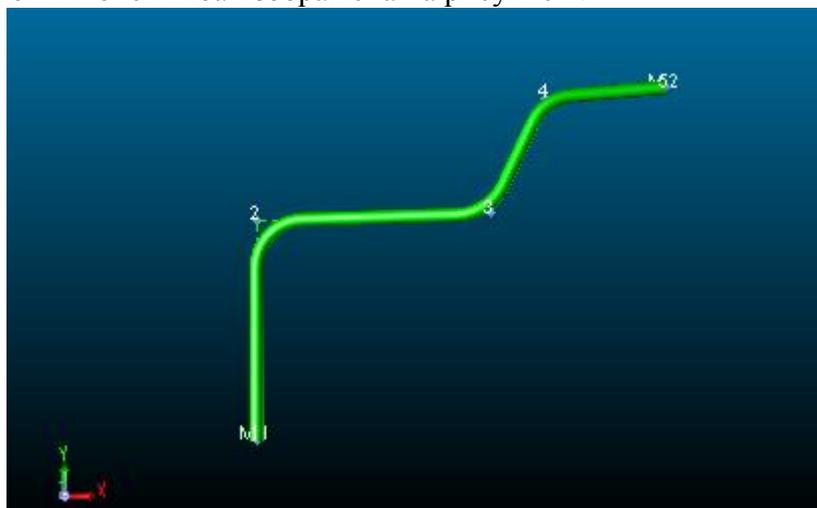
Мера Master –Tube для поверки систем измерительных оптических AICON TubeInspect и схема расположения точекгиба.
